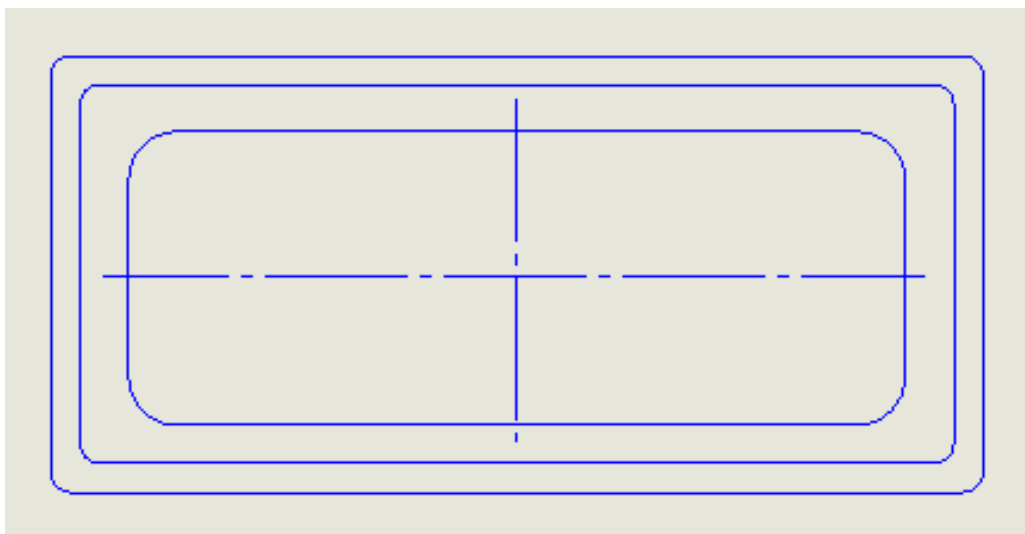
Dessine d'emboutissage de la table égouttoir.
